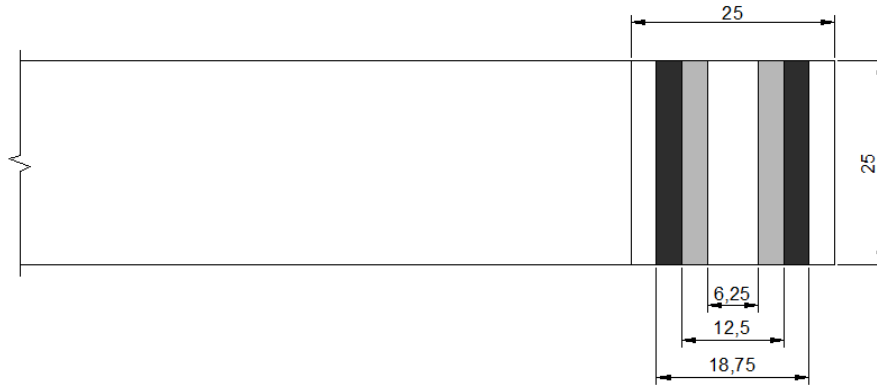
Localização e dimensões do defeito utilizado na junta de L_0 de 25 mm.
